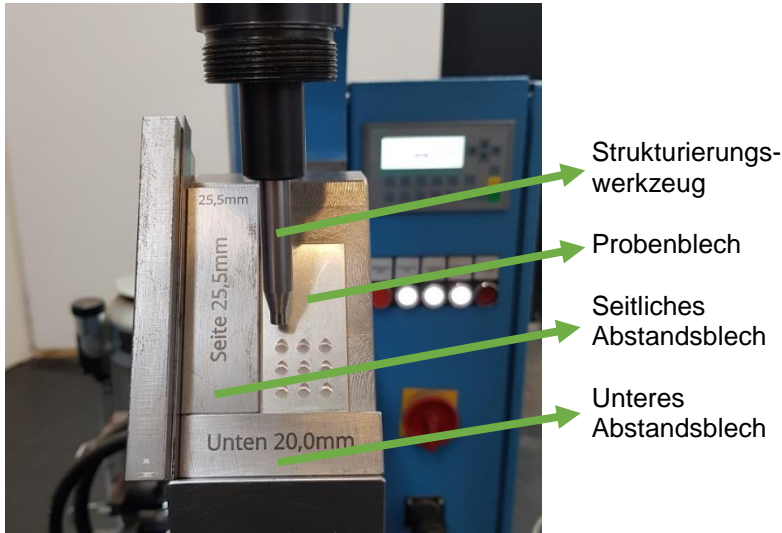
Universelle, hydraulische C-Bügel-Ständermaschine DFG 500/150 der Firma ECKOLD GmbH & Co. KG
